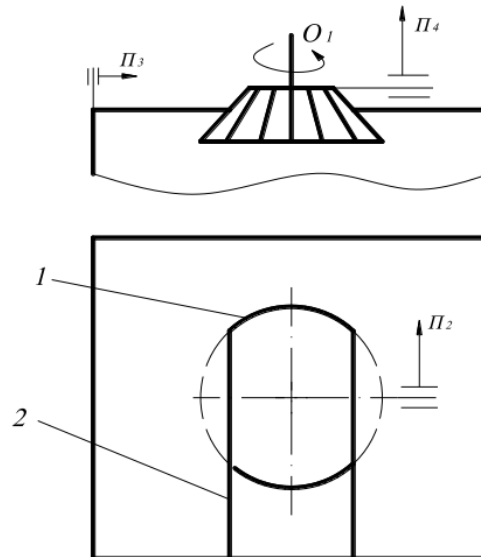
Оброблення фасонною фрезою складної поверхні
